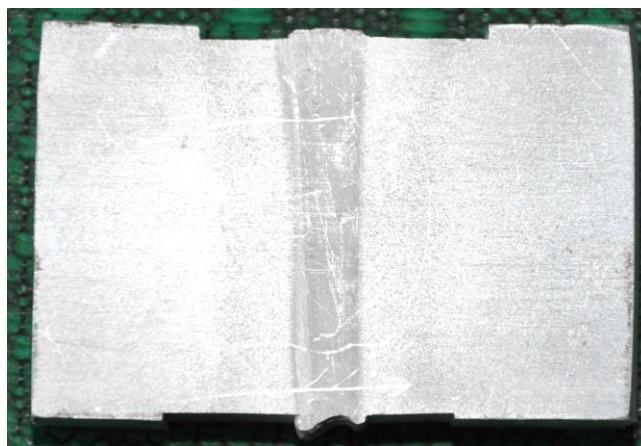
Макрошлиф сварного соединения ЭЛС $t=60$ мм.
